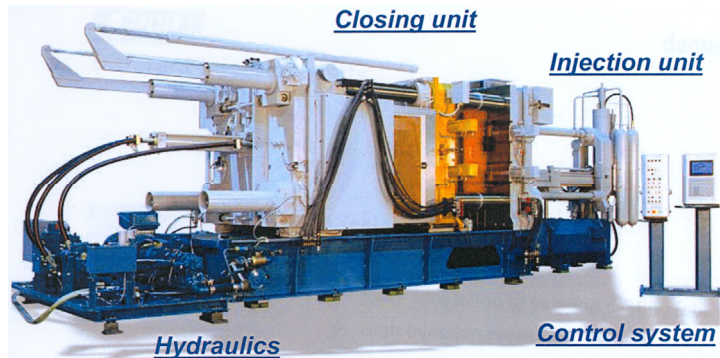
Machine de coulée sous pression Bühler servant à la fabrication de la mousse Combal® [KNO2004].
